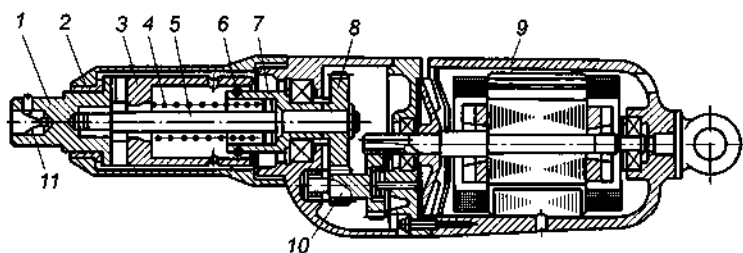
Ударно-импульсный электрогайковерт: 1 — рабочий наконечник; 2 — втулка; 3 — ведомая полумуфта; 4, 11 — пружины; 5 — шпindelь; 6 — шарик; 7 — ведущая полумуфта; 8, 10 — зубчатые колеса; 9 — корпус
